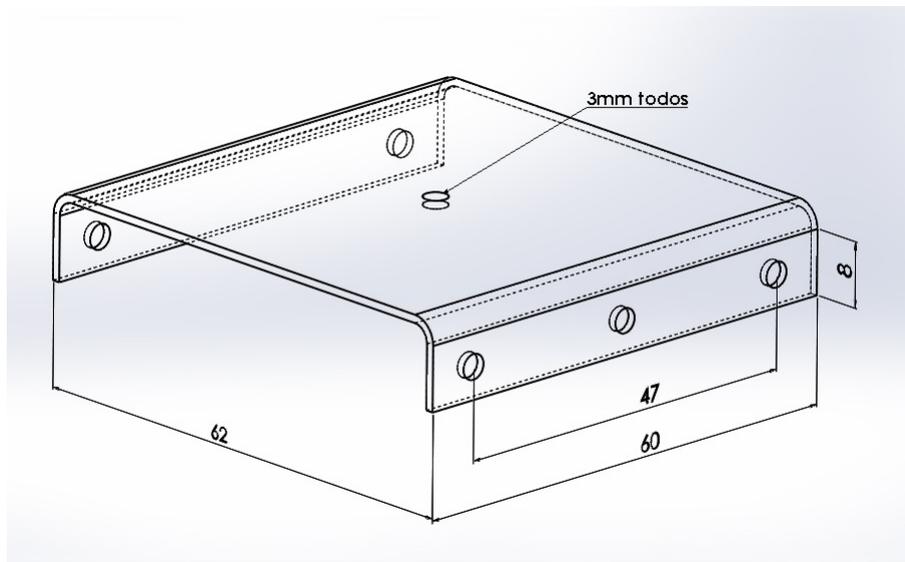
desenho técnico para auxiliar na construção do componente 1: carro de pesos.
